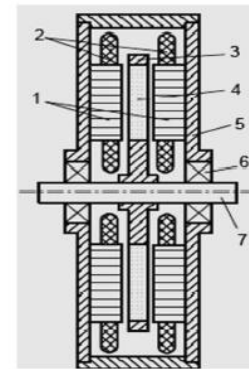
Descriptif de la machine à flux axial stator interne [13].
